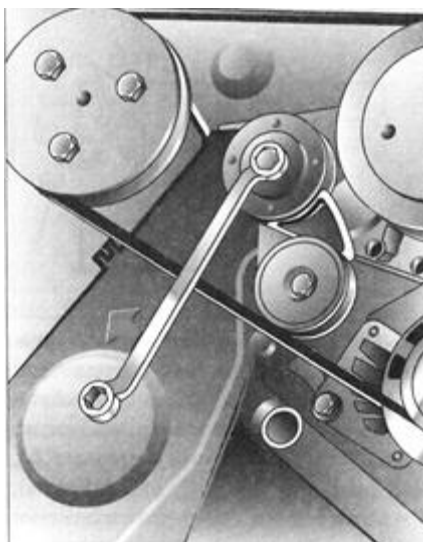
Натяжное устройство пружинного типа с натяжным роликом
